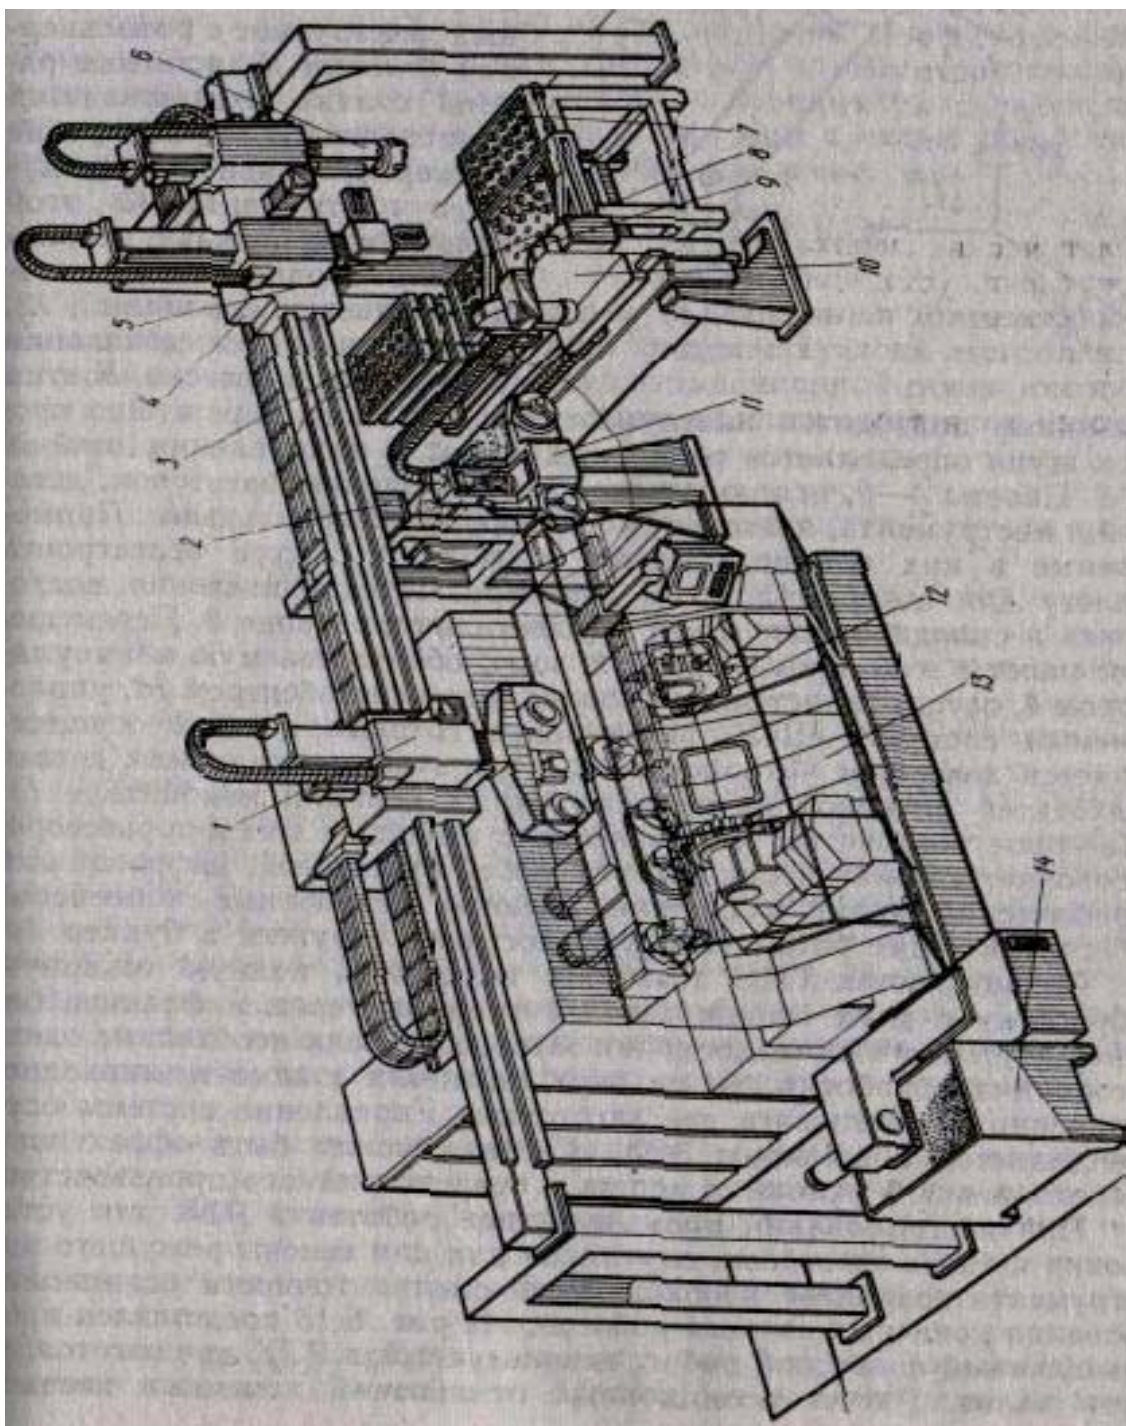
Гибкая производственная система для изготовления деталей тел вращения
